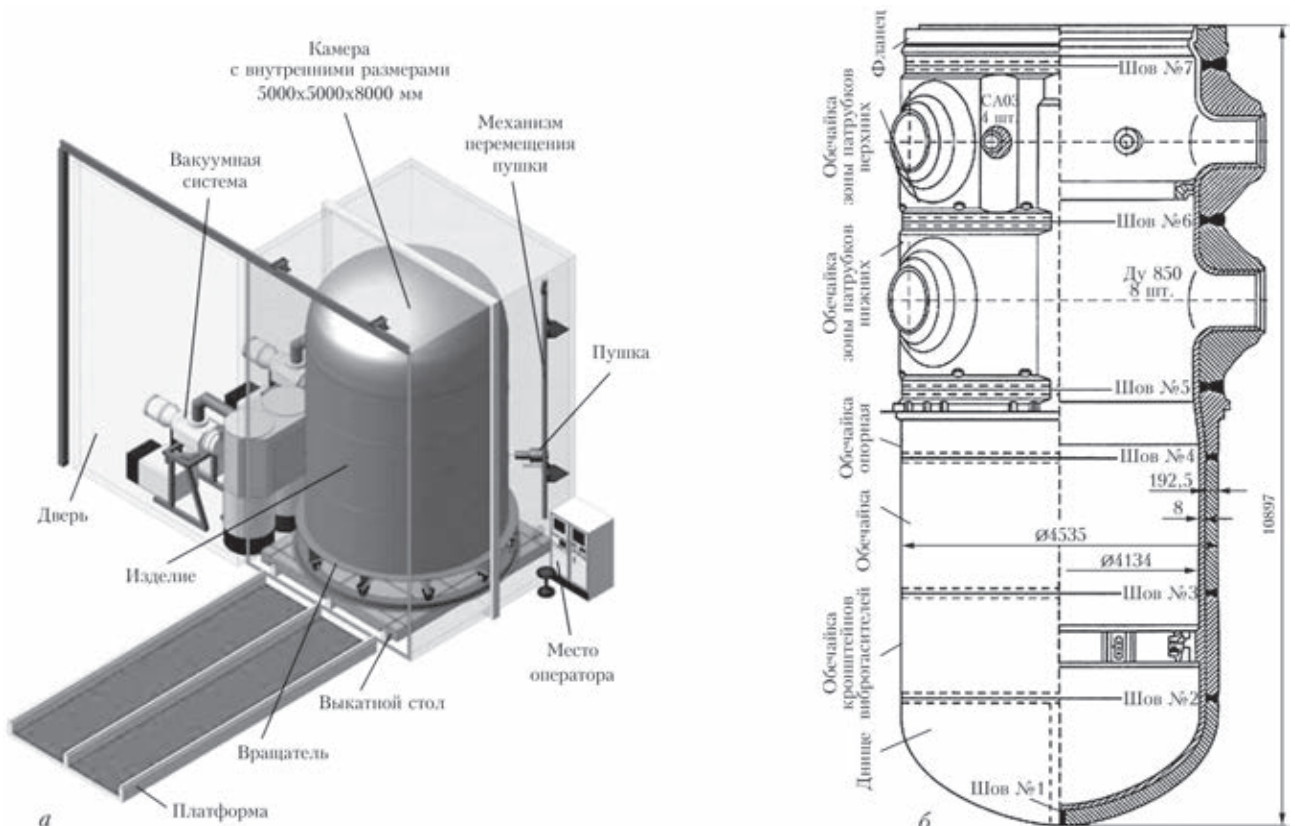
Принципиальная схема промышленной установки для ЭЛС кольцевых швов корпуса реактора ВВР-1000 (а) и схема корпуса реактора (б)
